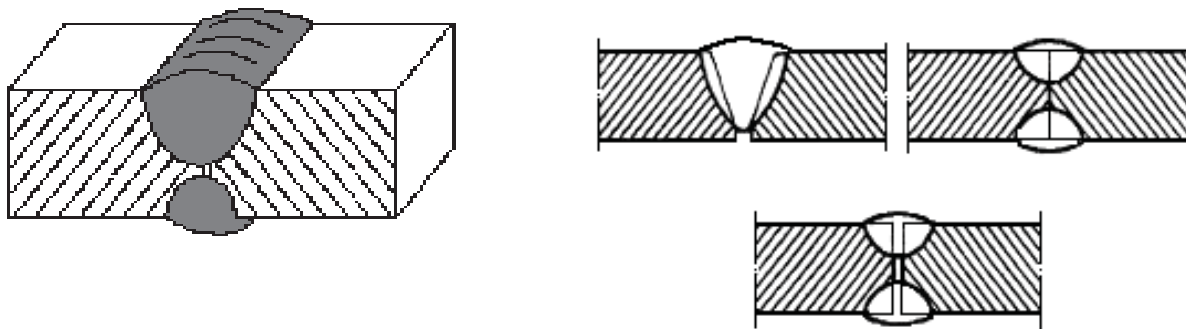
Схематичное изображение непровара сварного соединения
